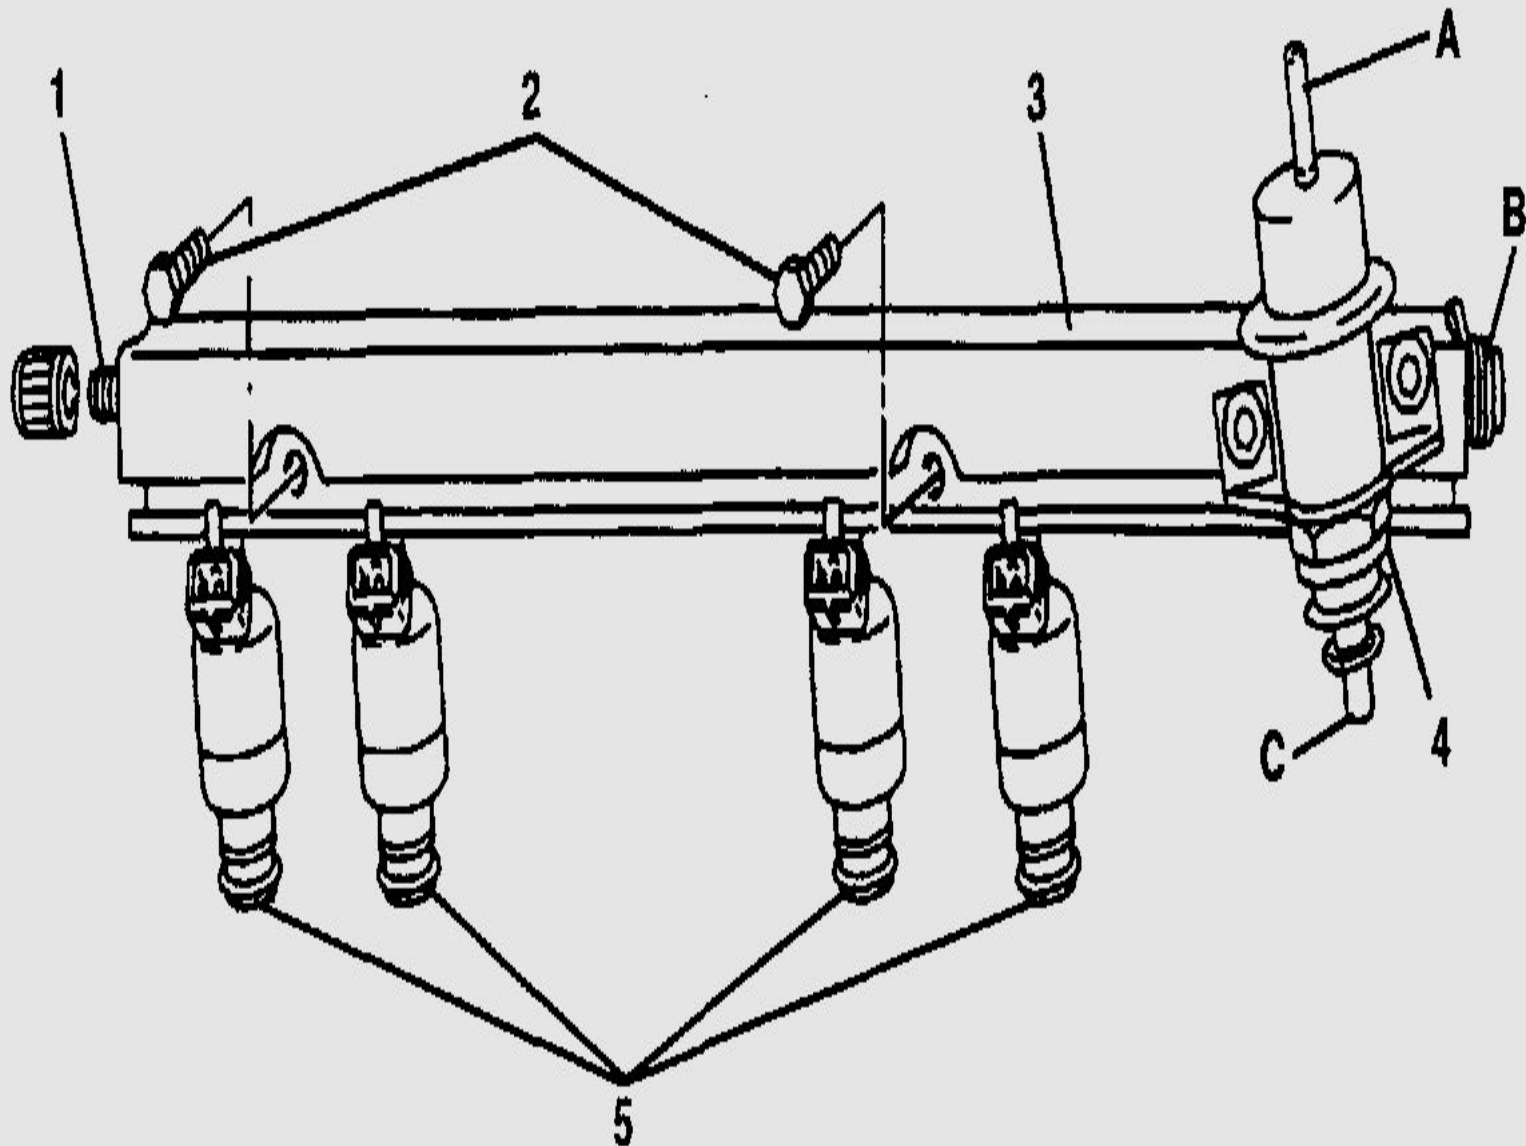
Рампа форсунок в сборе: 1 - штуцер для контроля давления топлива; 2 - болты крепления рамп; 3 - рампа форсунок; 4 - регулятор давления топлива; 5 - форсунки; А - патрубок отбора разрежения из впускной трубы; В - штуцер для подвода топлива; С - штуцер для слива топлива
